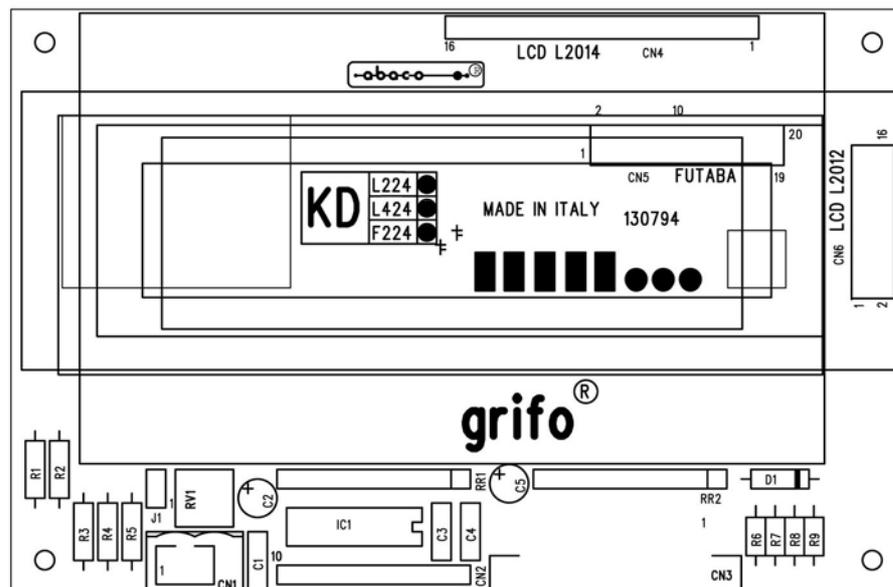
PIANTA COMPONENTI DELLA KDX-xxx (LATO SALDATURE)
